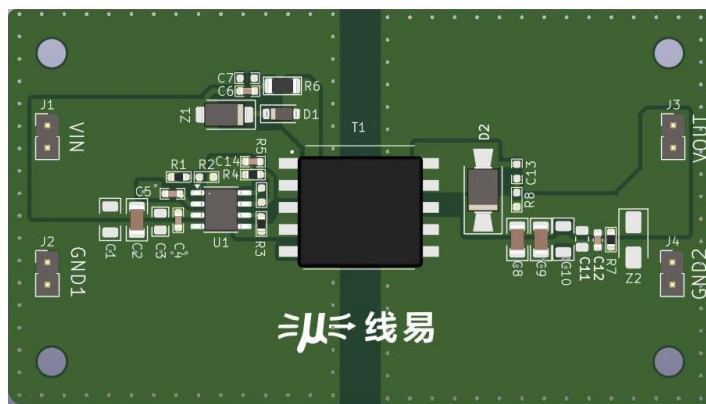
PCB 示意图 (尺寸: 45 x 80mm)
